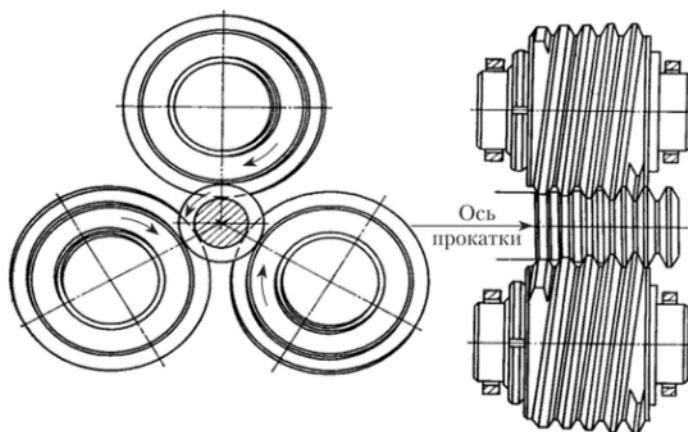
Схема непрерывного накатывания резьбы на винтах неограниченной длины
